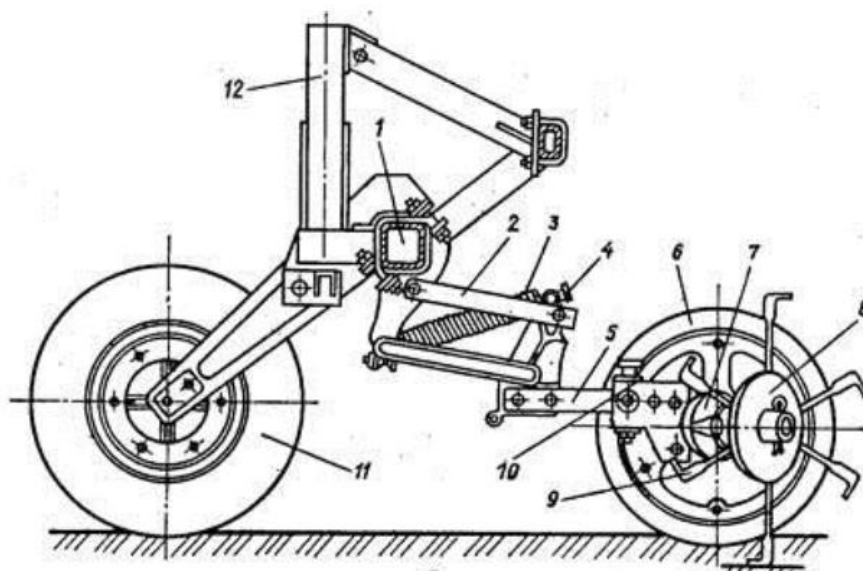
Схема розпушувача УСМП - 5,4: 1 – брус; 2 – паралелограмний механізм; 3 – пружина; 4 – гвинт; 5 – планки гряділя; 6 – опорно-приводне колесо; 7 – редуктор; 8 – ріжуча головка; 9 – ніж; 10 – корпус; 11 – опорне колесо; 12 – рама.
